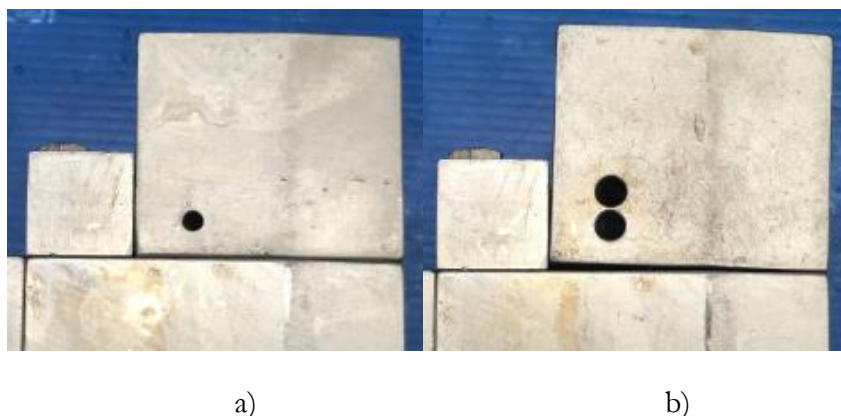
Válvula de enchimento: a) escape original, b) escape com *upgrade*.
